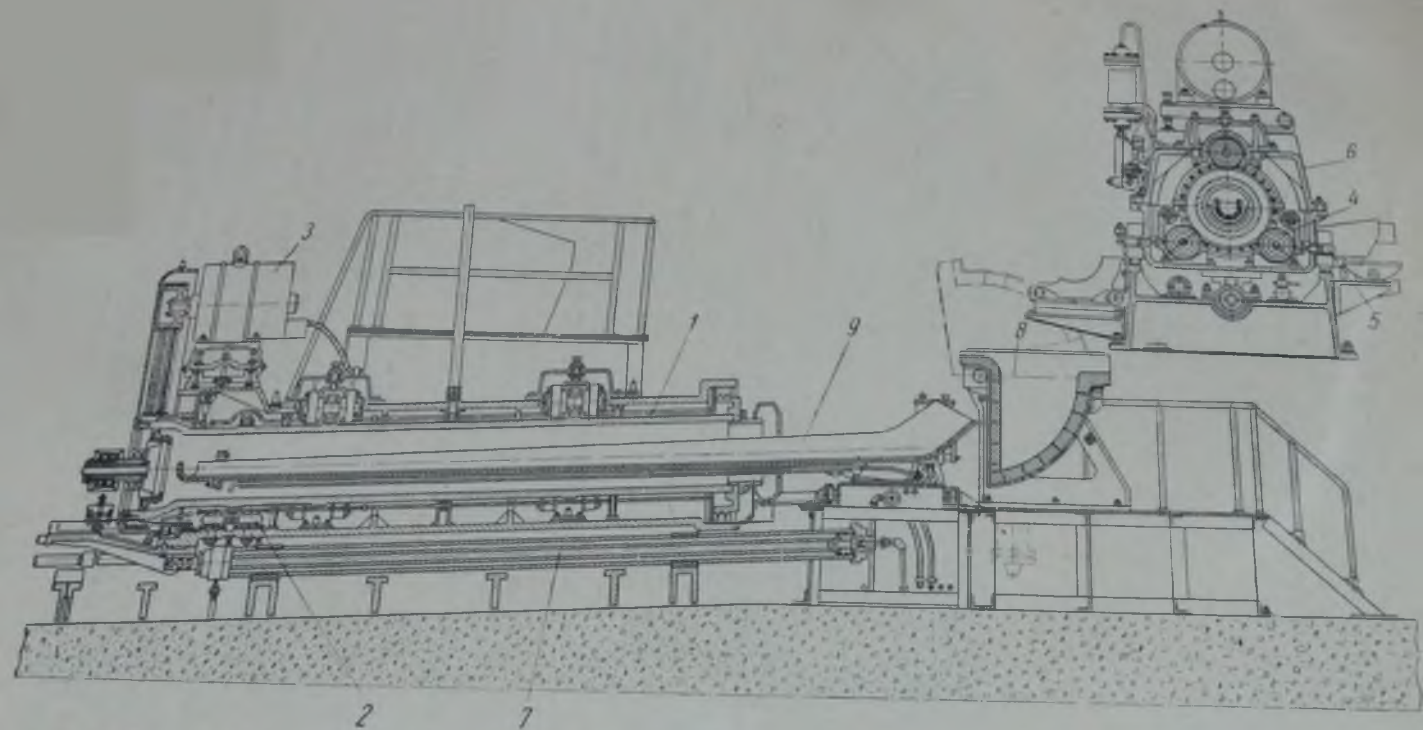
Центробежная машина для отливки труб в металлические формы конструкции НИИЛитмаш
